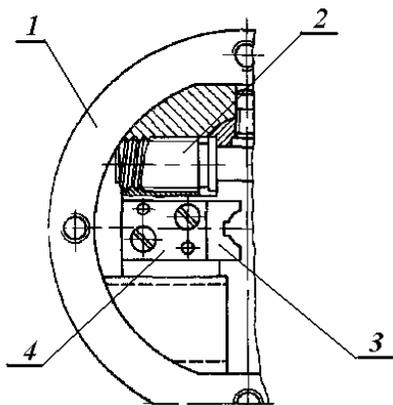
37 - Схема конструкции двухкулачкового самоцентрирующего патрона
